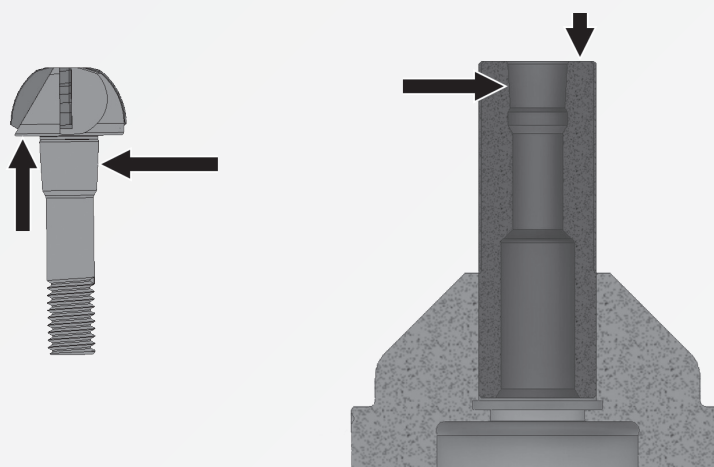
Kegel- und Planflächen am Kugelbahnfräser und der Aufnahme reinigen
